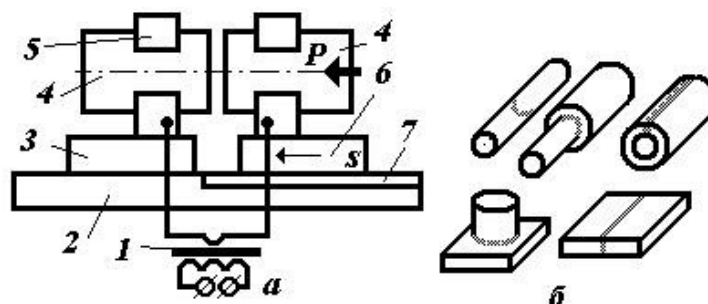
Стыковая контактная сварка: а – схема установки; б – типовые заготовки; 1 - трансформатор; 2 – станина; 3 – неподвижная плита; 4 – заготовки; 5 - зажимы; 6 – подвижная
